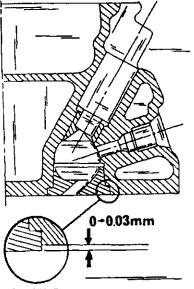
Предкамеры должиы выступать над поверхностью головки цилиндров на указанный размер.
